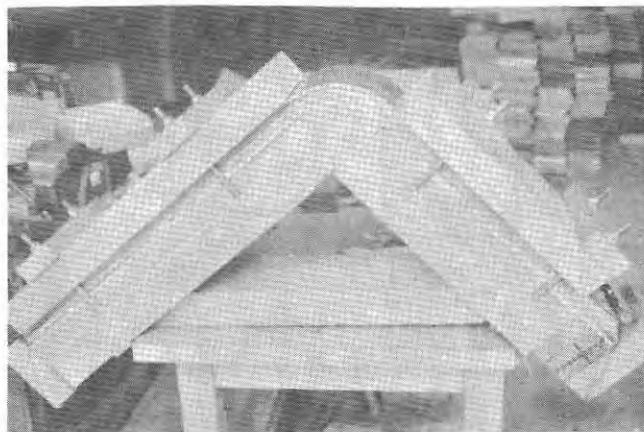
Molde para a construção da peça de apoio do encosto da cadeira.
